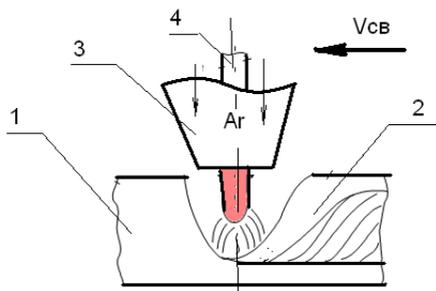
Схема процесса сварки металла погруженной дугой:
